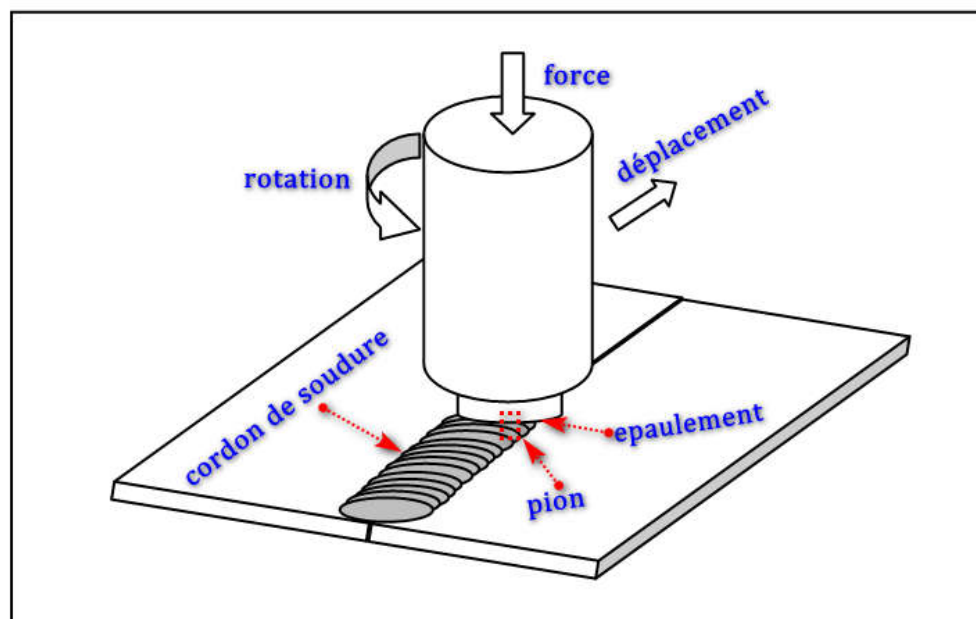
Représentation schématique du procédé de soudage FSW.
